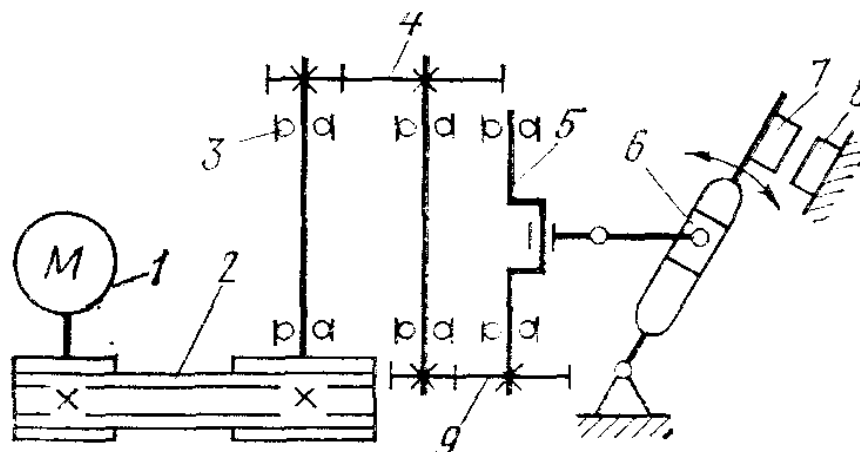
Кинематическая схема станка СМЖ.-172А: 1 — электродвигатель; 2 — клиноременная передача; 3 — подшипниковые опоры; 4, 9—зубчатые передачи; 5—эксцентриковый вал; 6—кулиса; 7, 8 — подвижный и неподвижный ножи
